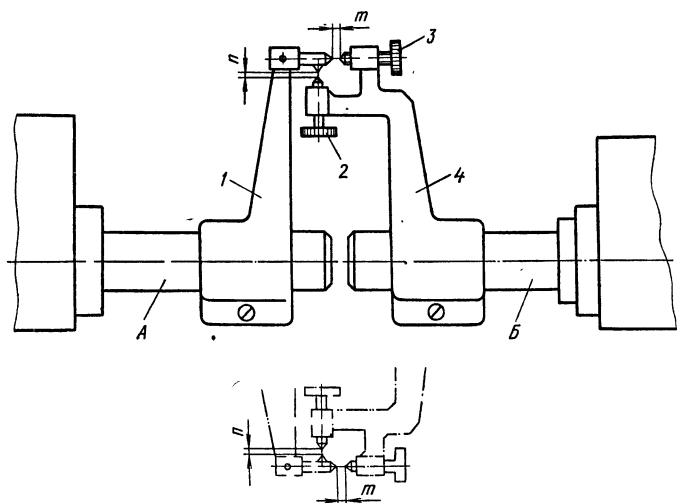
Схема проверки соосности валов с помощью специального поворотного приспособления
